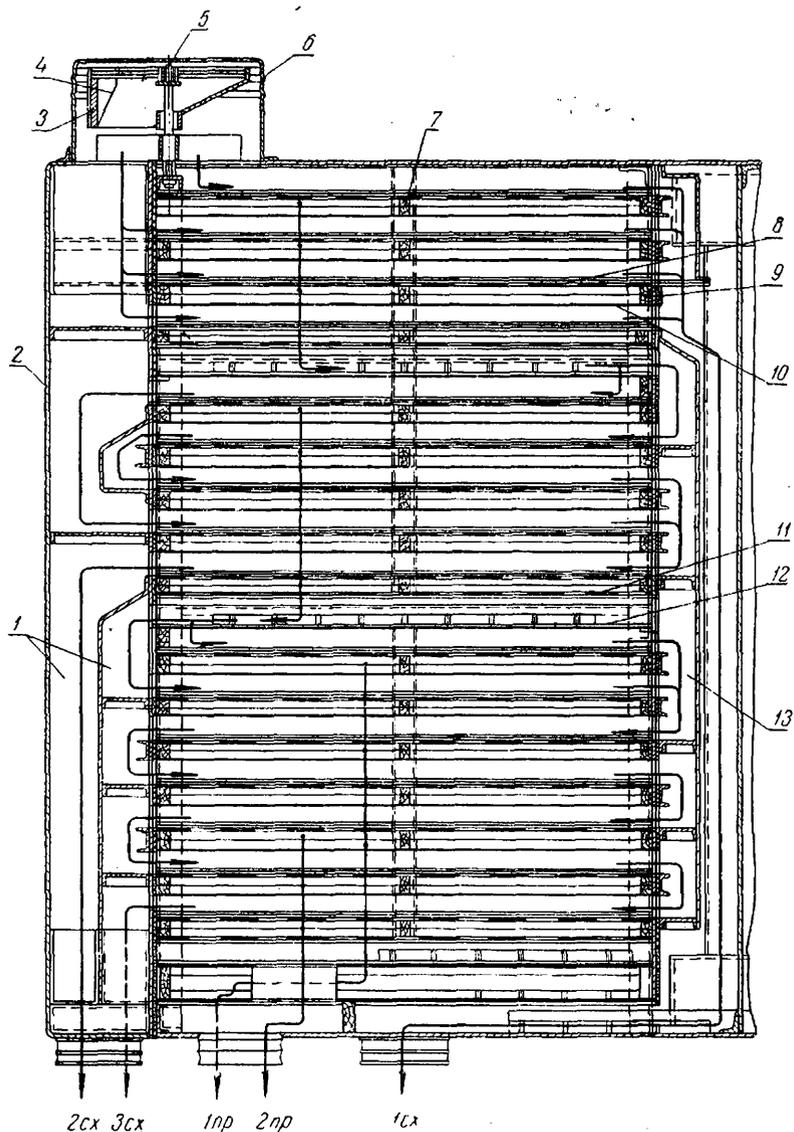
Ситовой корпус рассева ЗРШ-6.
